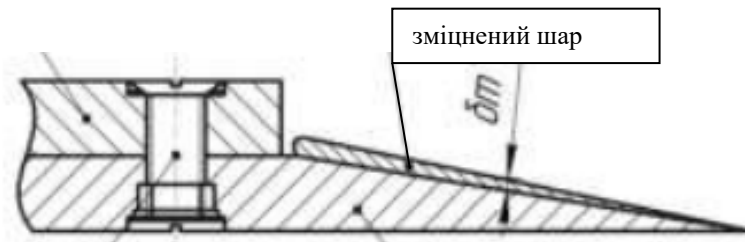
Переріз конструкції диска борони з робочою ріжучою поверхнею зубів, що має можливість заміни [17]
